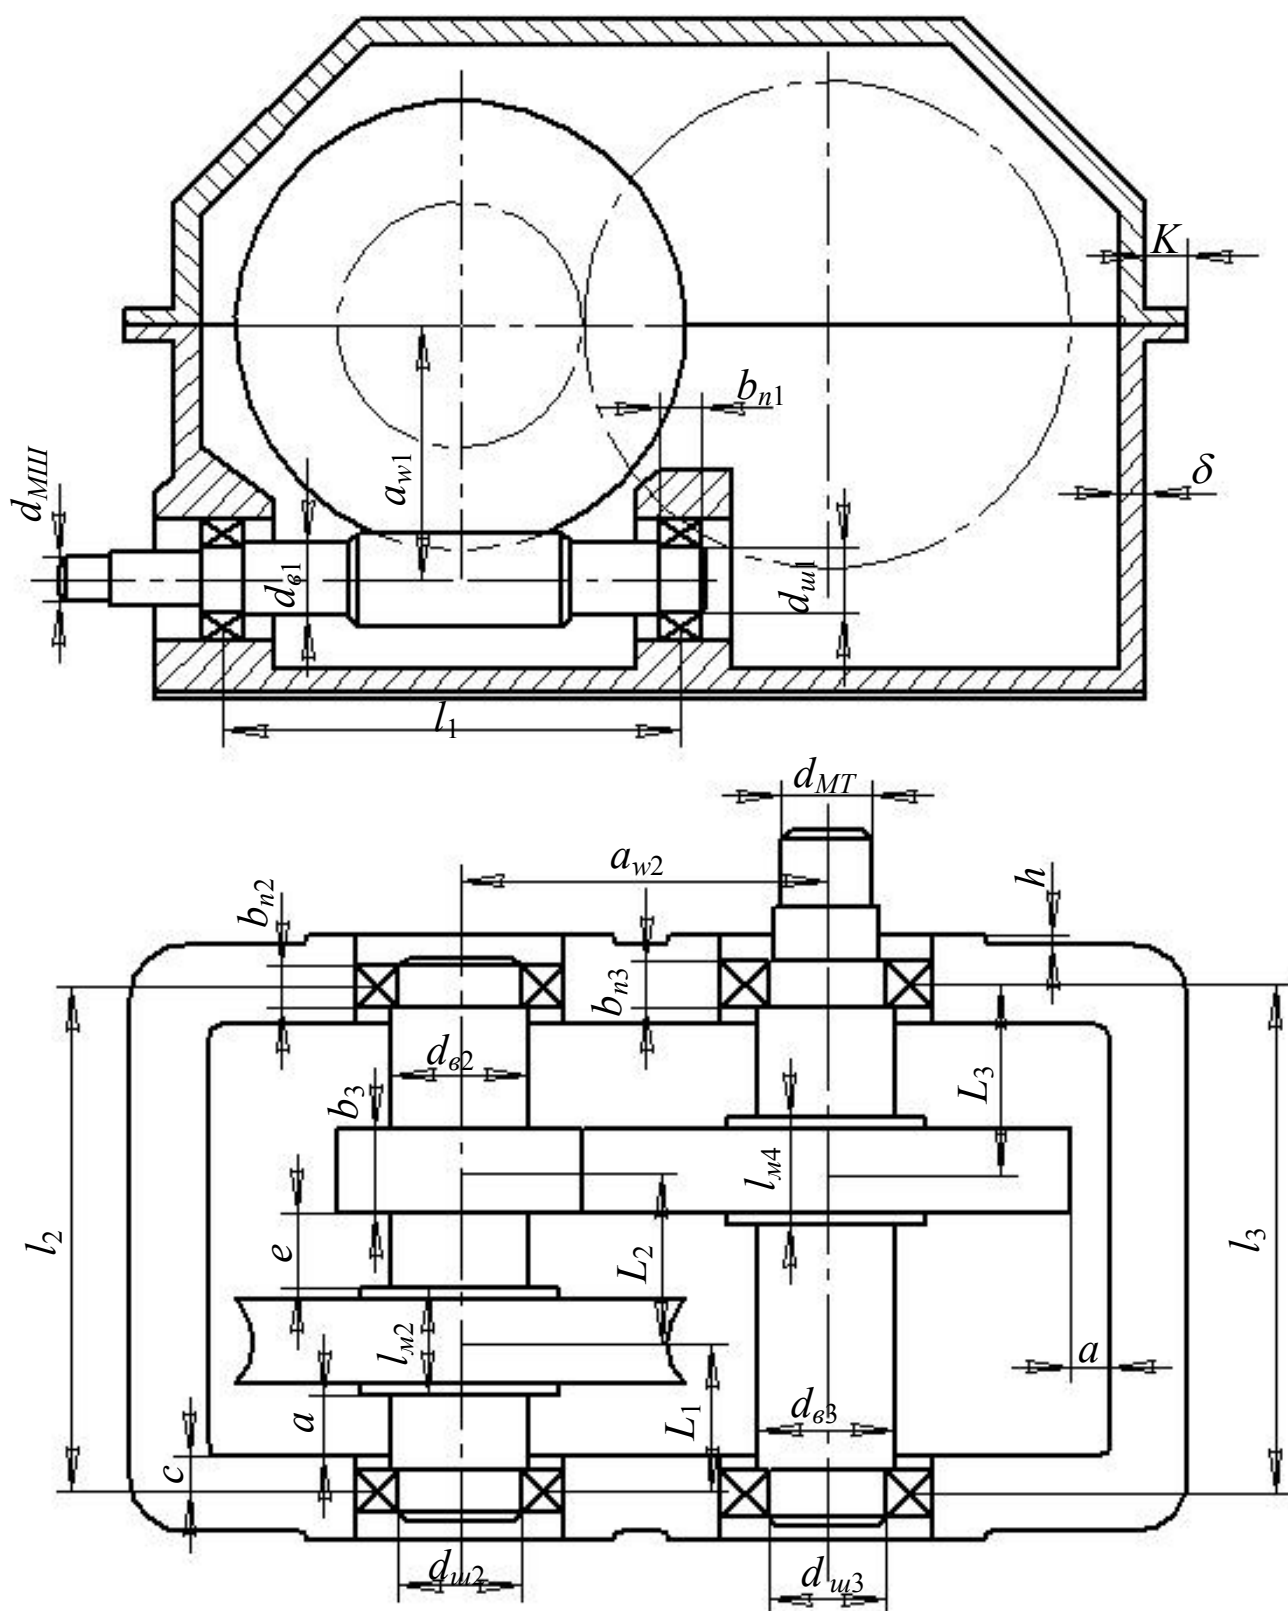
Эскизная компоновка червячно-цилиндрического двухступенчатого редуктора с нижним расположением червяка
